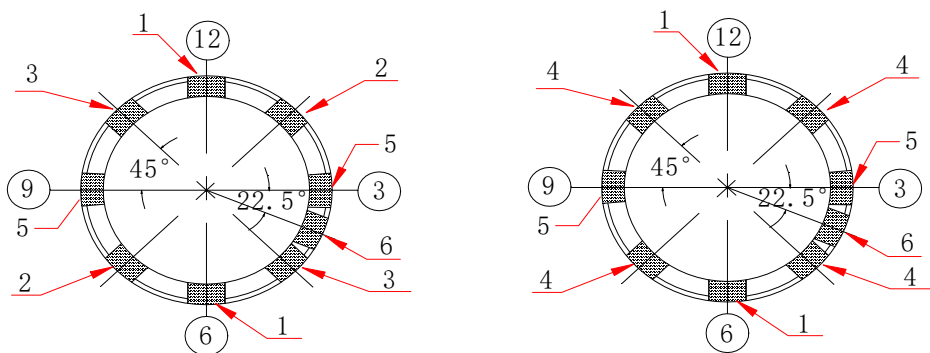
圆管对接接头焊接工艺评定试件及试样取样位置
